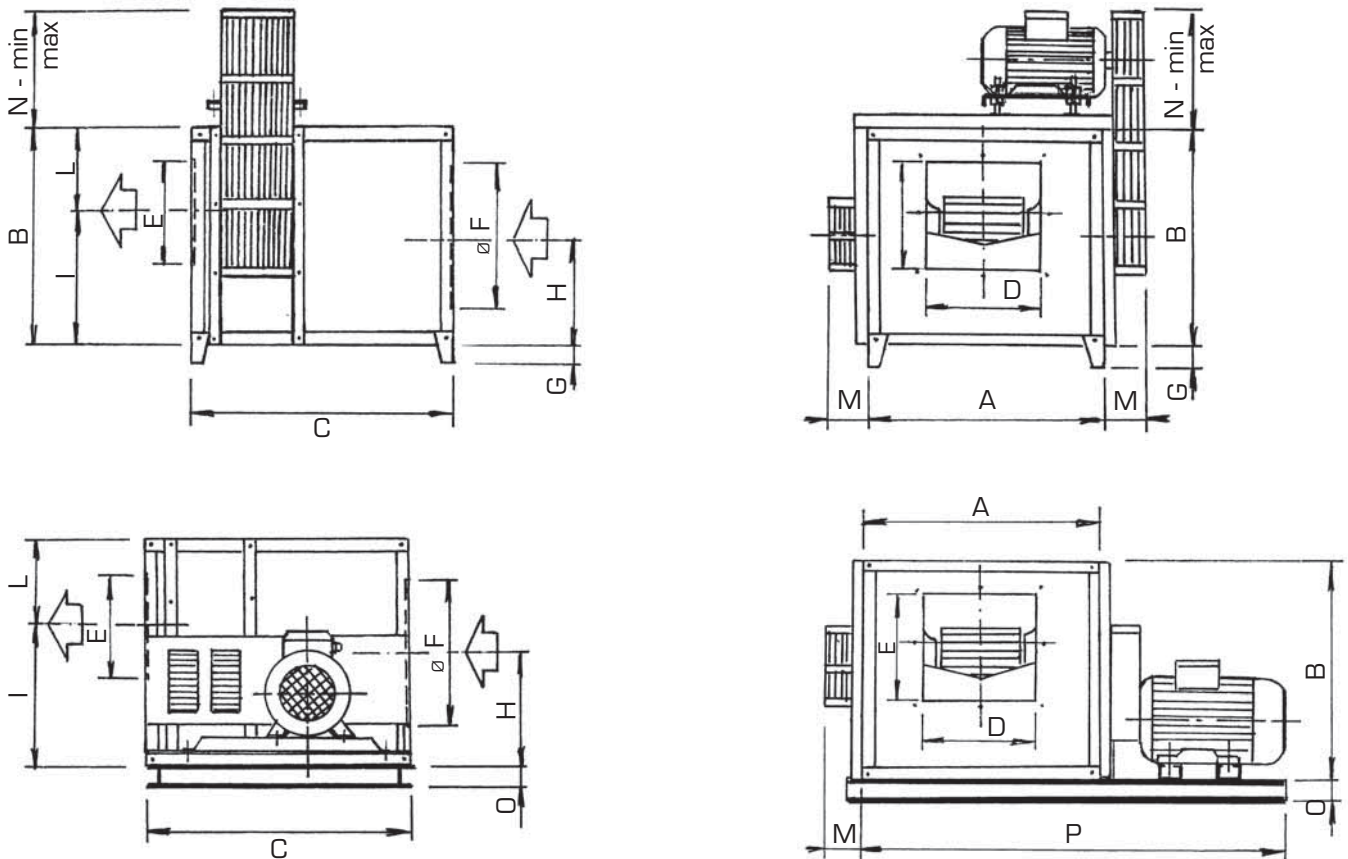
Cassonati con motori da 11 Kw e oltre - Caissons with motor up to 11 Kw and more
